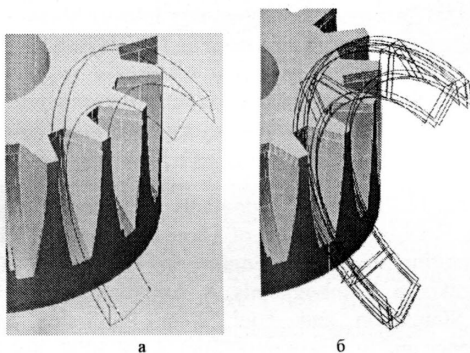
Траєкторія руху - тороїд окремого зубця фрези (а) та композиція з тороїдів, які формують поверхню різання цього зубця (б)
